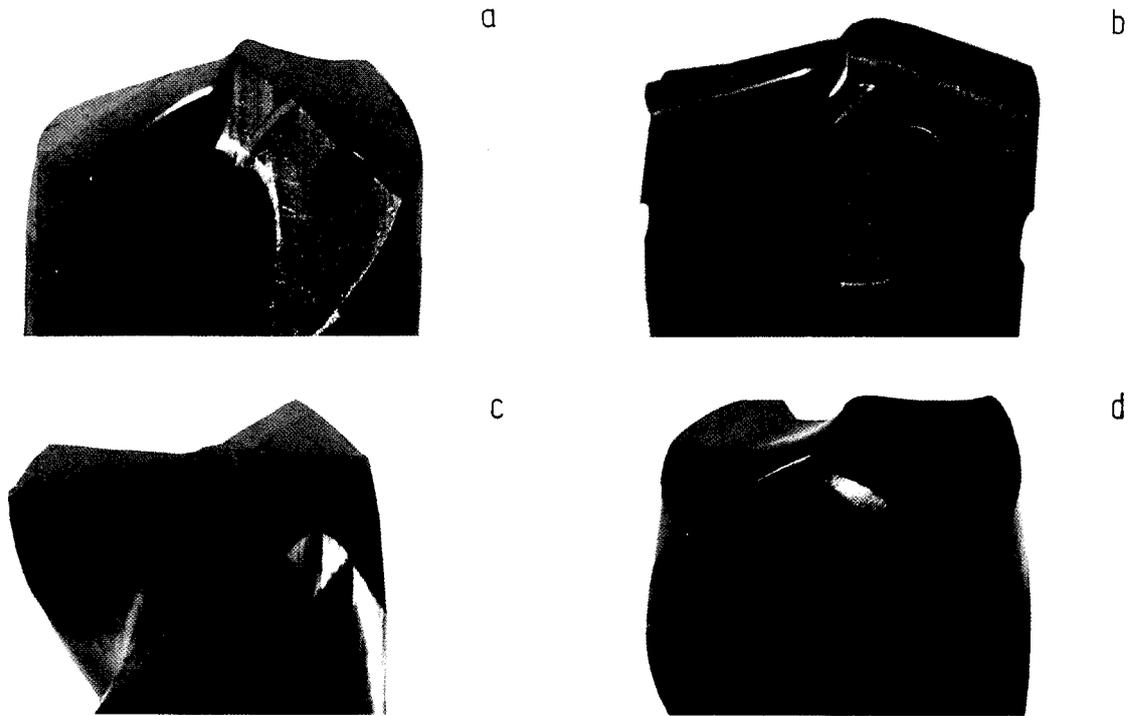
Ausführungen von Voll-Hartmetall-Bohrern für die Stahlbearbeitung
